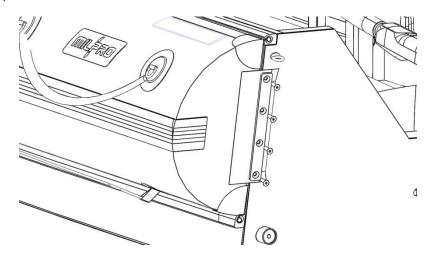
MONTAGE DU FLOTTEUR 4 FIGURE 3.1.1.2.4 – TUBE INSTALLATION 4
